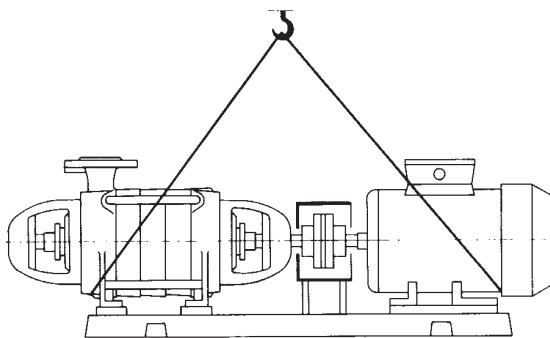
Транспортировка насосного агрегата с горизонтальным размещением
